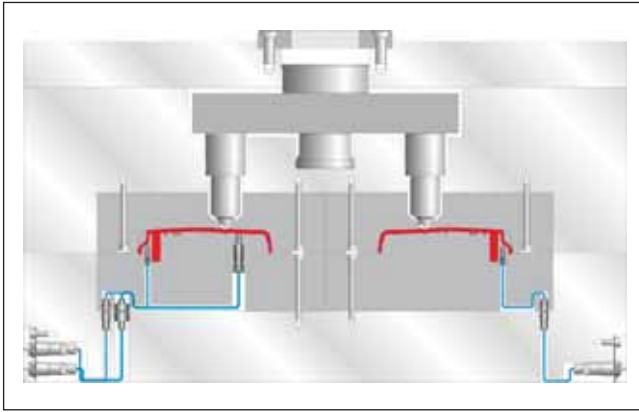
Schnellkupplungen für Werkzeuginnendruck- und Werkzeugwandtemperatur-Sensoren ermöglichen einen schnellen und automatischen Austausch von Werkzeugeinsätzen
